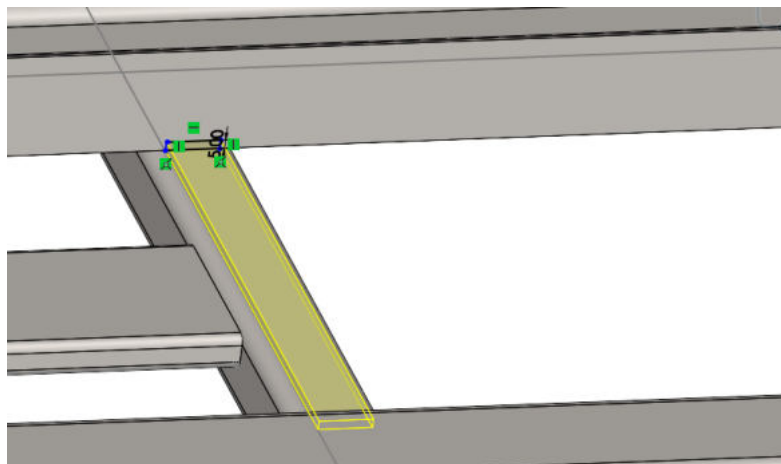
Croquis de la solución aportada para el refuerzo de las vigas transversales.
